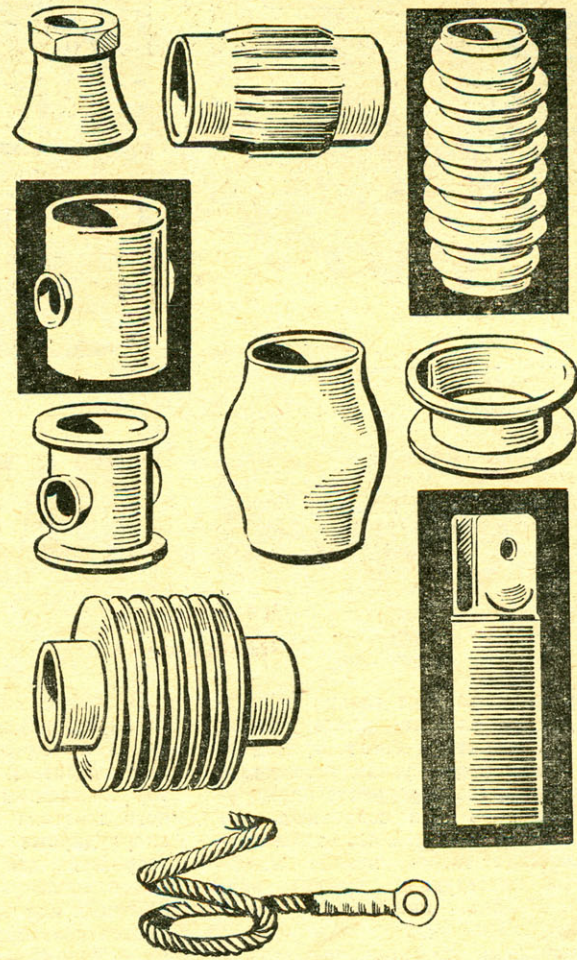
Образцы деталей, получаемых методом магнитной штамповки.
